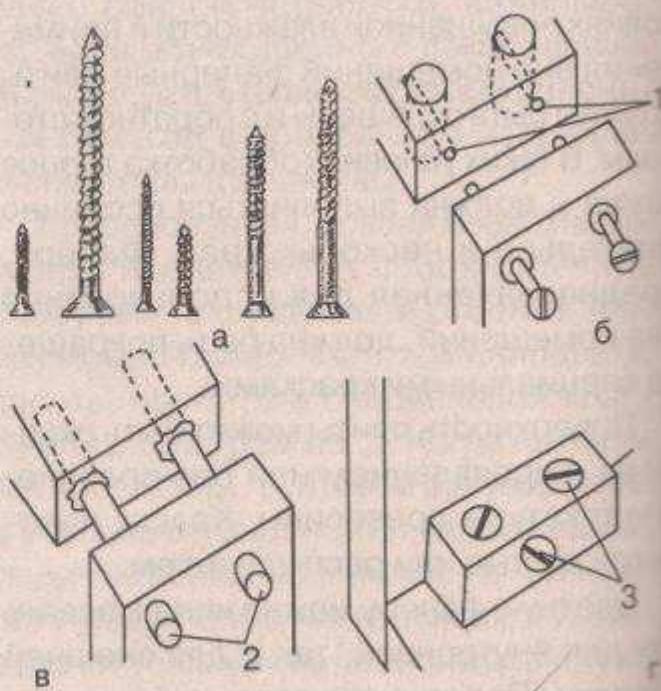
Соединения древесностружечных плит: а — шурупы: слева: четыре шурупа самореза различной величины; справа: два обычных шурупа для дерева (для ДСП не подходят); б — соединение на деревянных пробках: 1 — пробка; в — соединение на круглых шипах: 2 — шипы; г — соединительная фурнитура: 3 — шурупы
